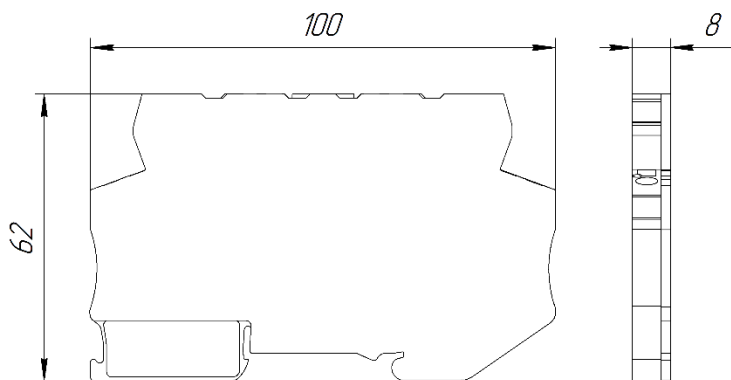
Габаритный чертеж преобразователя в компактном слотовом корпусе
